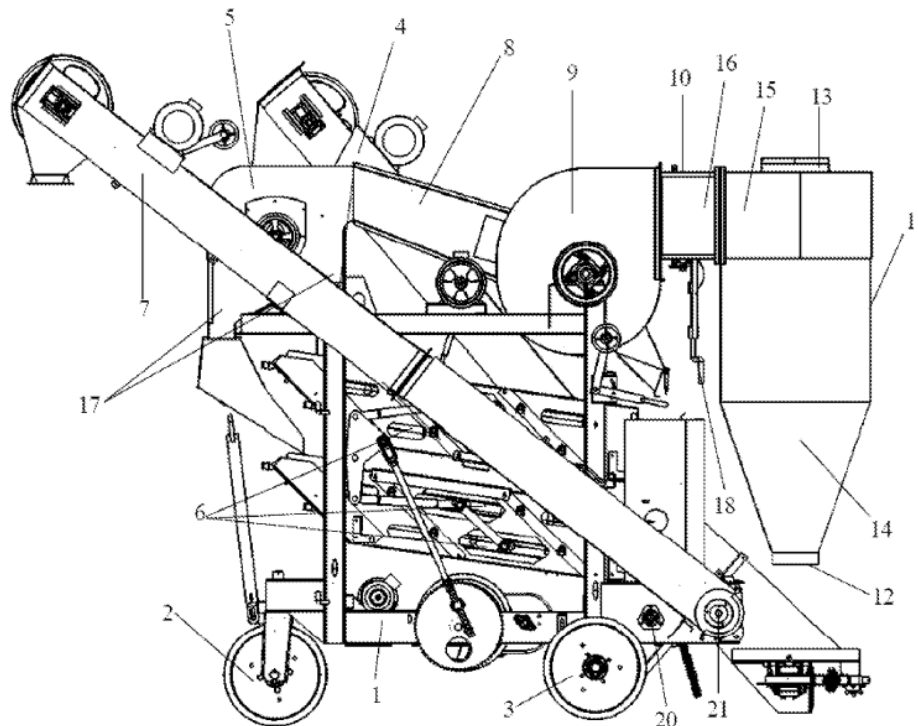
Загальний вигляд очисника вороху: 1 – рама; 2 – керуючі колеса; 3 – ходові колеса; 4 – транспортер завантажувальний; 5 – бункер; 6 – решітні стани; 7 – транспортер вивантажувальний; 8 – повітропровід; 9 – витяжний вентилятор; 10 – напрямний модуль; 11 – циклон; 12 – вихідний отвір; 13 – вихід для чистого повітря; 14 – нижня частина циклону; 15 – бічна частина циклону; 16 – бічна стінка; 17 – канали аспіраційні; 20 – фуражний шнек; 21 – шнек чистого зерна.
